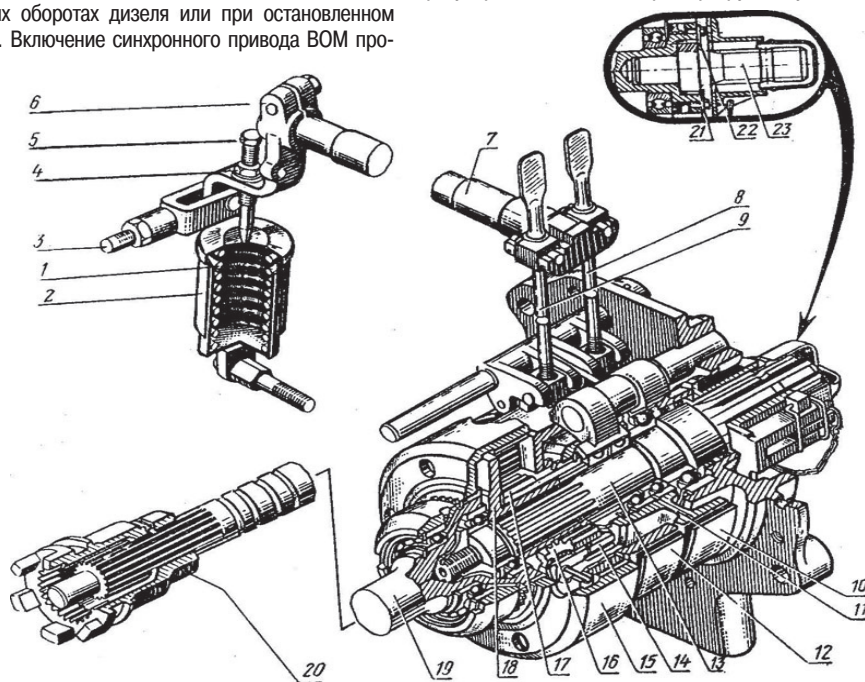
Планетарный редуктор заднего ВОМ. 1 — пружина цилиндрическая; 2 — стакан; 3 — тяга; 4 — контргайка; 5 — болт упорный; 6 — рычаг упорный; 7 — валик управления; 8, 9 — винты регулировочные; 10, 12 — лента тормоза с фрикционной накладкой; 11 — барабан включения ВОМ; 13 — вал заднего ВОМ; 14 — ось сателлита; 15 — шестерня коронная; 16 — сателлит; 17 — шестерня солнечная; 18 — водило (в сборе с тормозным барабаном); 19 — вал коронной шестерни; 20 — муфта переключения привода; 21 — болт; 22 — стопорная шайба; 23 — сменный хвостовик.
